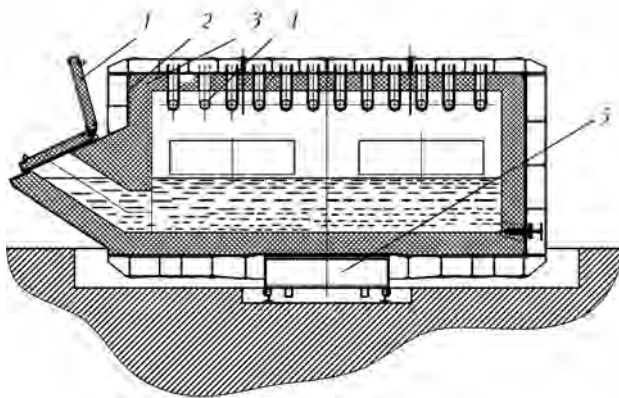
Камерная электропечь-миксер типа САМП: 1 – заливочная крышка; 2 – кожух; 3 – футеровка; 4 – нагревательные элементы; 5 – МГД перемешиватель
